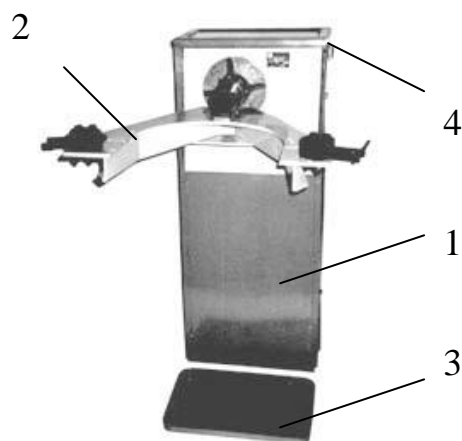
Стенд для разборки и сборки редукторов задних мостов Р-640:
